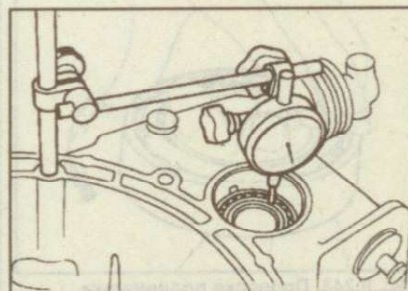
Использование индикатора стрелочного типа для измерения люфта подшипника дифференциала
